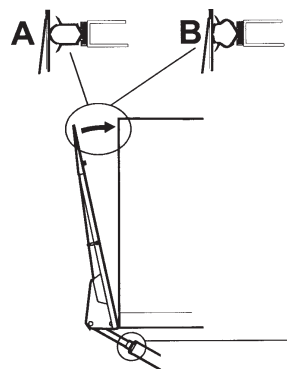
Kofferaufbau ohne Hecktüren. Mit Seitendichtungen.
